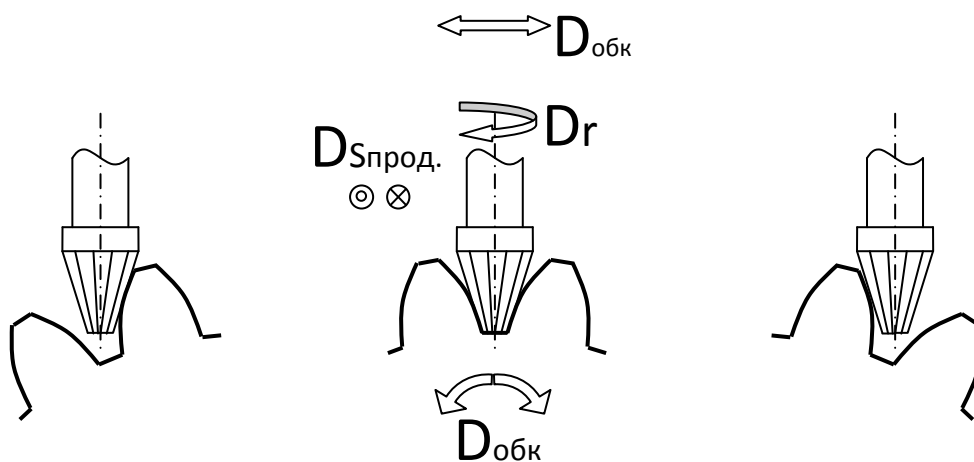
Кинематика формообразующих движений при нарезании прямозубых цилиндрических колес пальцевой реечной фрезой
